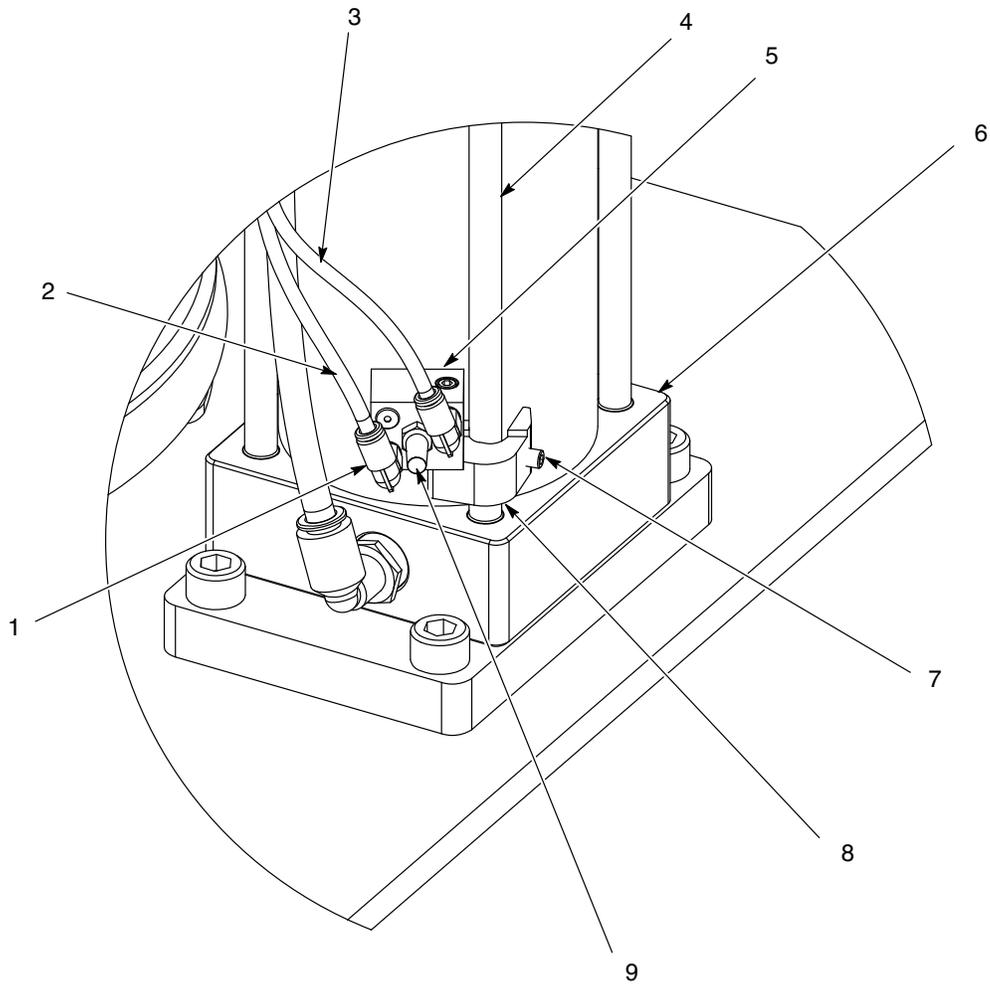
Baugruppe Rahmen/Kolbensensor
